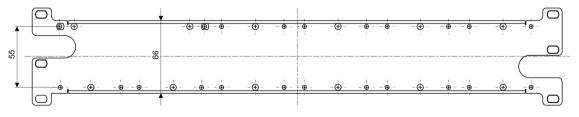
Ширина вырезов и схема сверления отверстий – устройство 1/1, второй ряд устройств
